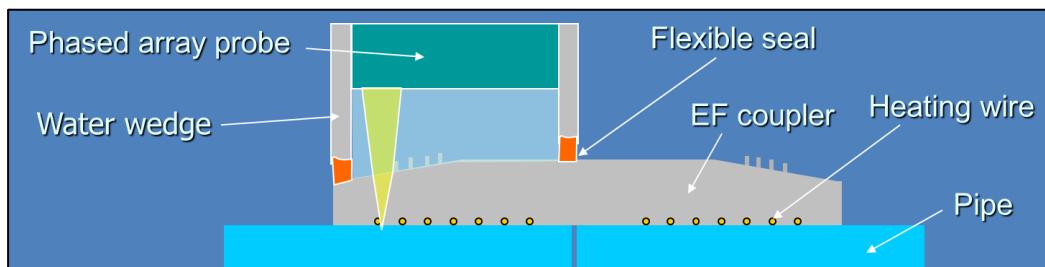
Esquema de inspección de soldaduras por electrofusión
